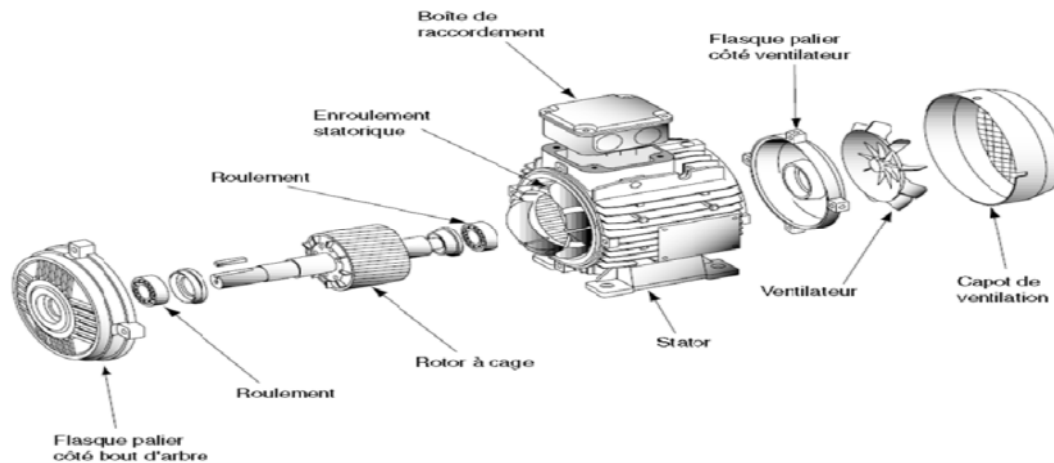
Vue éclatée d'une machine asynchrone à cage d'écureuil [17]
